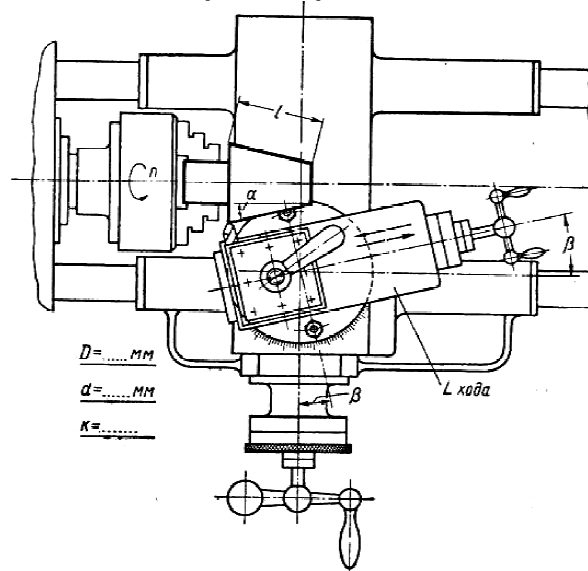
Схема наладки токарного станка на обработку конуса при повернутых верхних салазках
